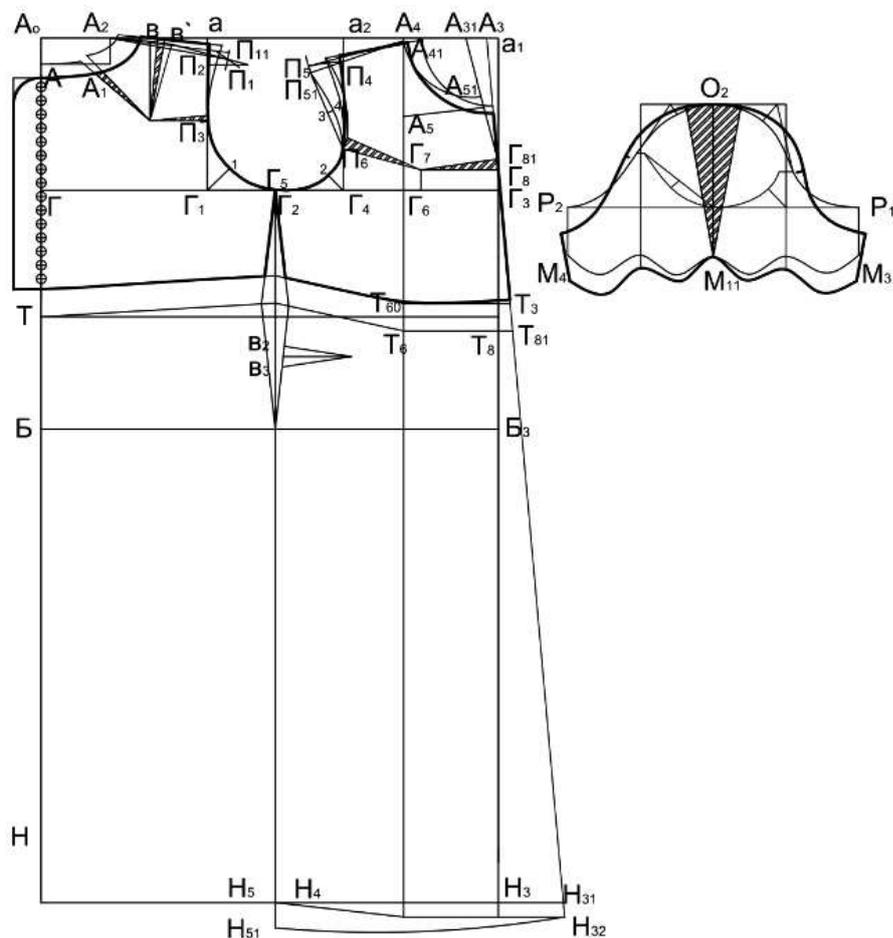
Чертеж БК и ИМК детского платья для девочки
